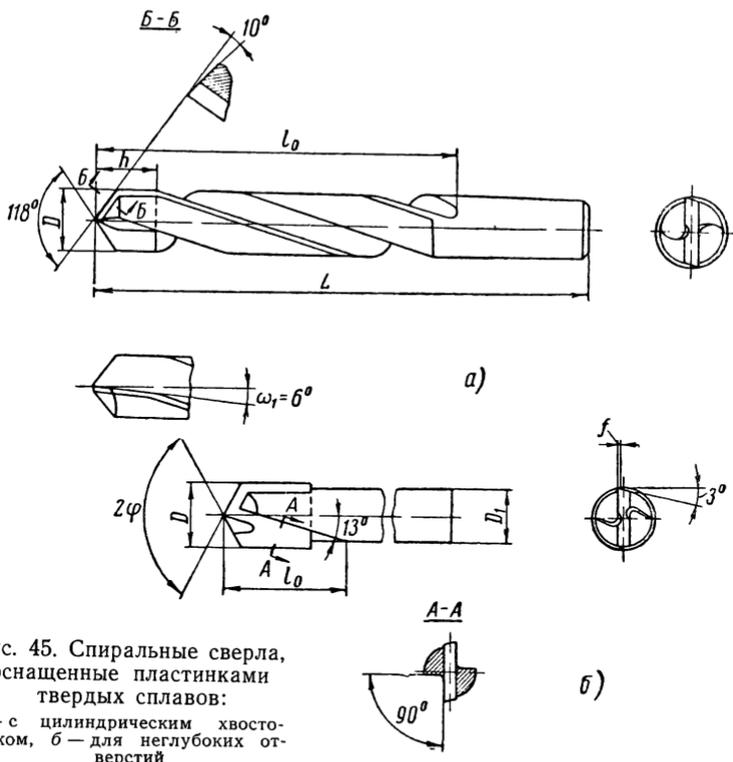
Спиральные сверла, оснащенные пластинками твердых сплавов:
